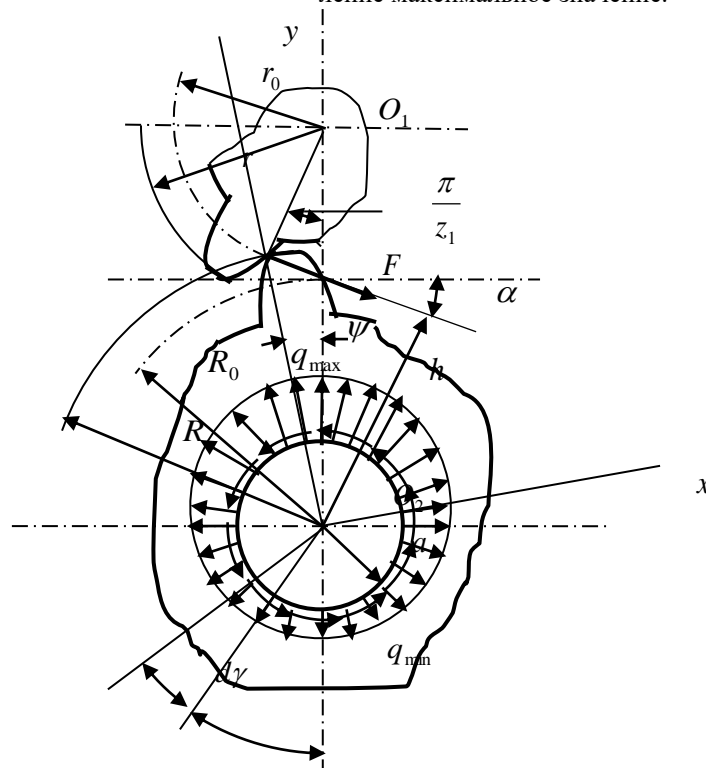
Зацепление цилиндрических зубчатых колес с прямыми зубьями
